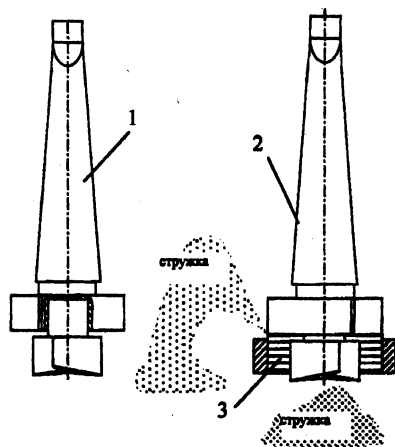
Двухрезцовая развертка-фреза: 1 – общий вид; 2 – в процессе обработки; 3 – подшипник скольжения на основе древесины
